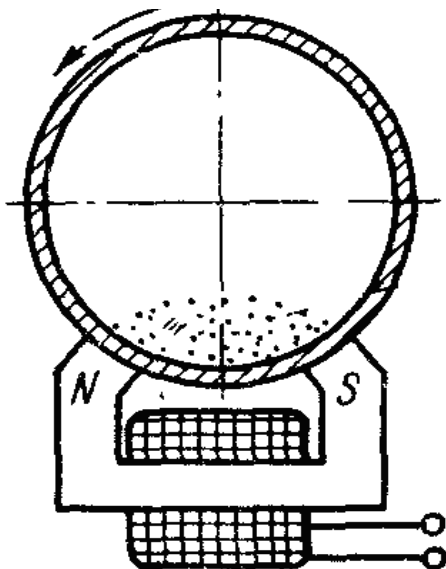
Схема МАО внутренних поверхностей деталей
